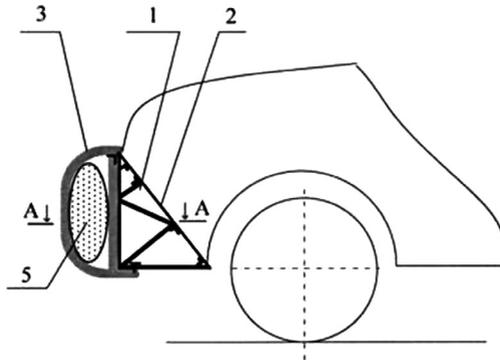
Автомобильный бампер (вид сбоку): 1 – несущая балка; 2 – металлический лист; 3 – наружный гибкий корпус; 5 – упругие амортизирующие элементы
